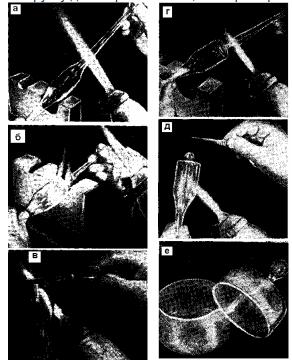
Изготовление стаканчика для взвешивания: а—разогревание пульни и придание ей конусообразной формы с помощью обкатки; б—формирование корпуса и крышки на обкатке; в — выравнивание разверткой дна; г—прикрепление к крышке порции стекла; д — формирование держателя на крышке с помощью пинцета; е — готовое изделие.
